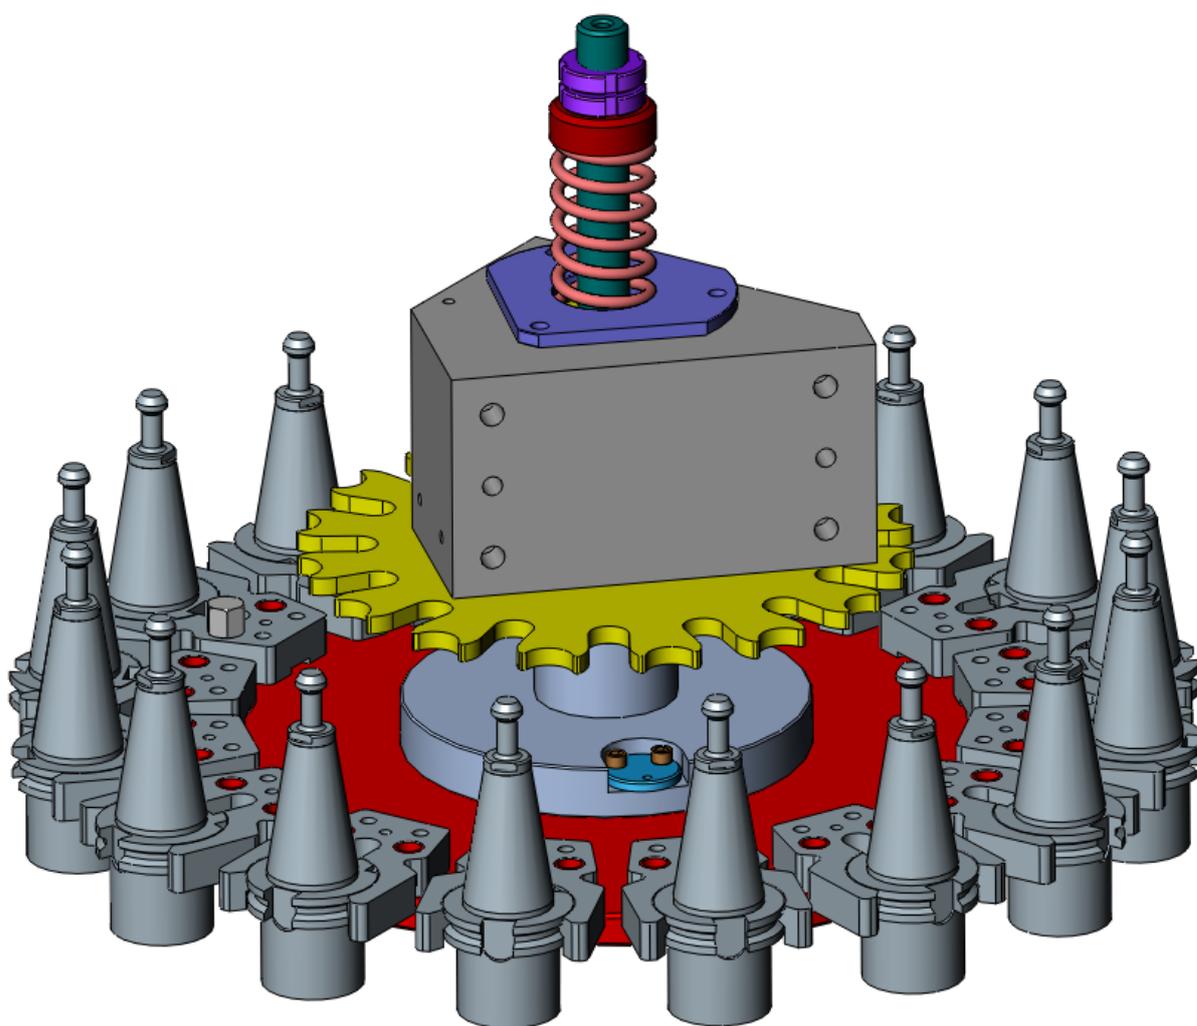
Инструментальный магазин станка модели 400V
